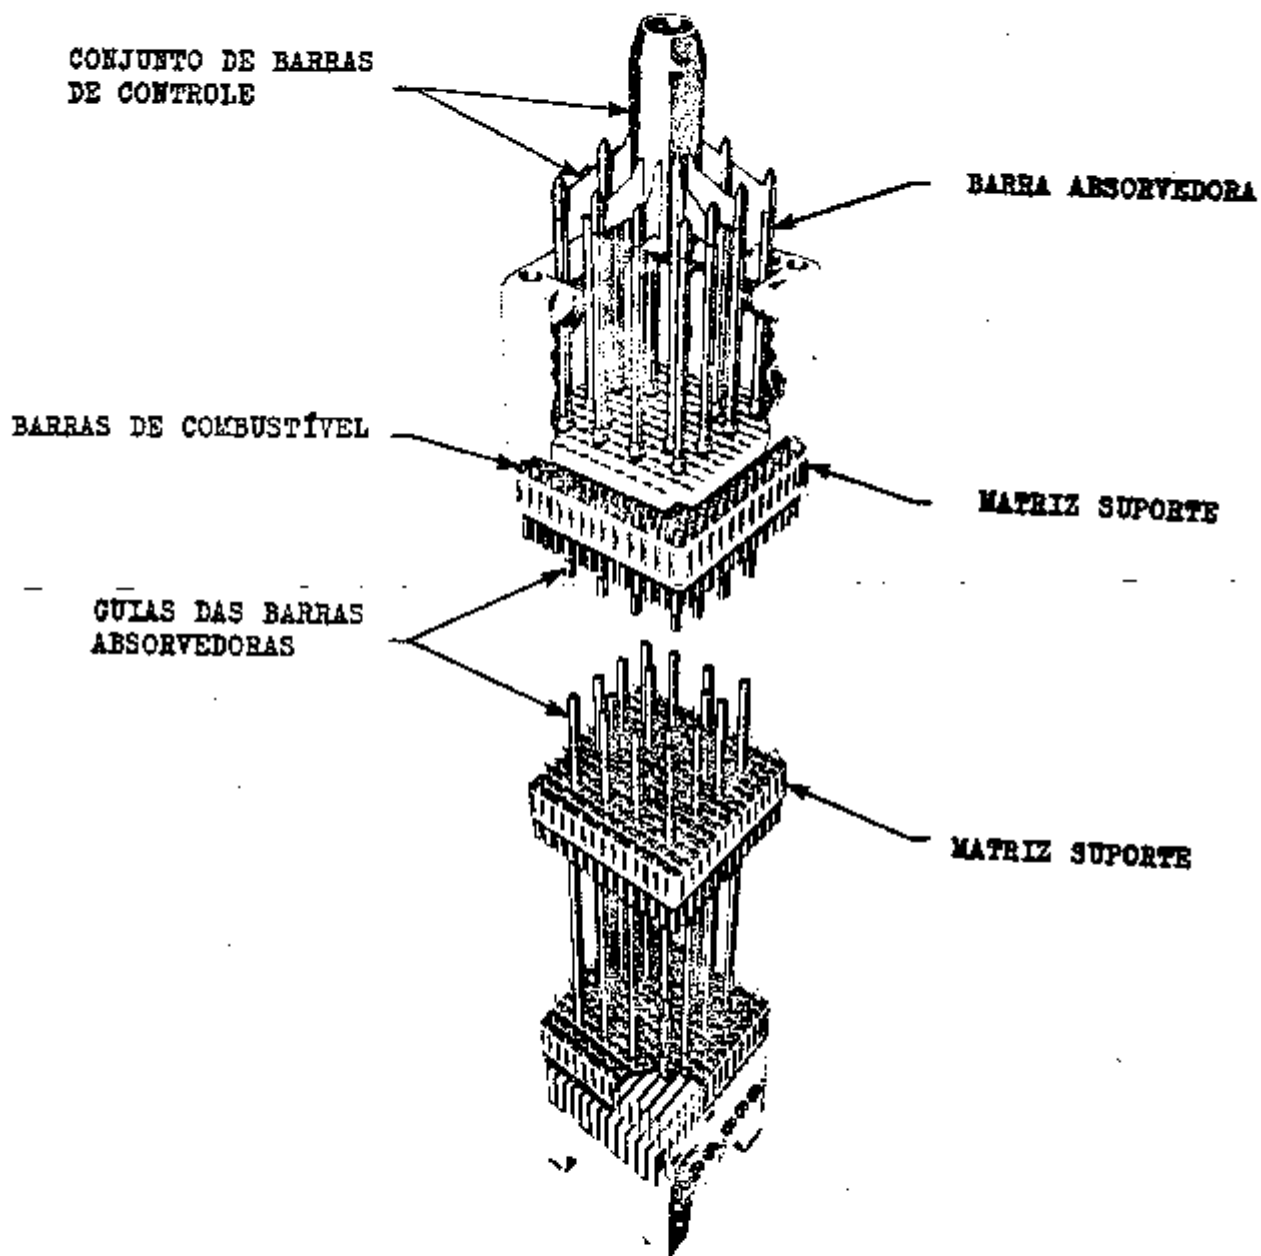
CONJUNTO DE COMBUSTÍVEL DO PWR
